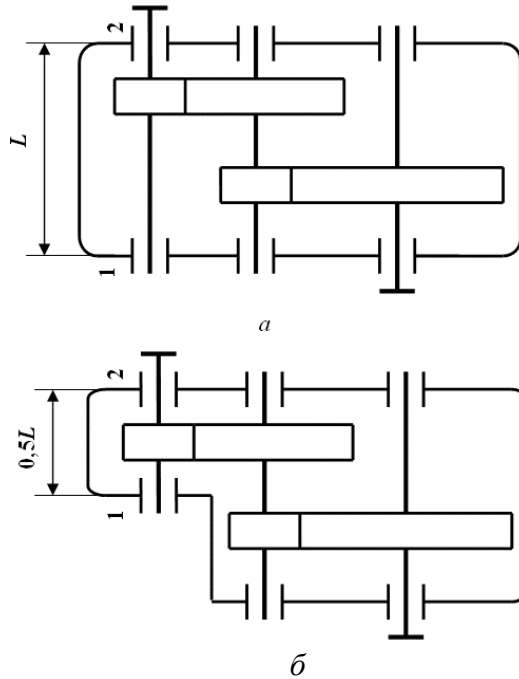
Конструктивна схема корпусу двохступеневого редуктора:
